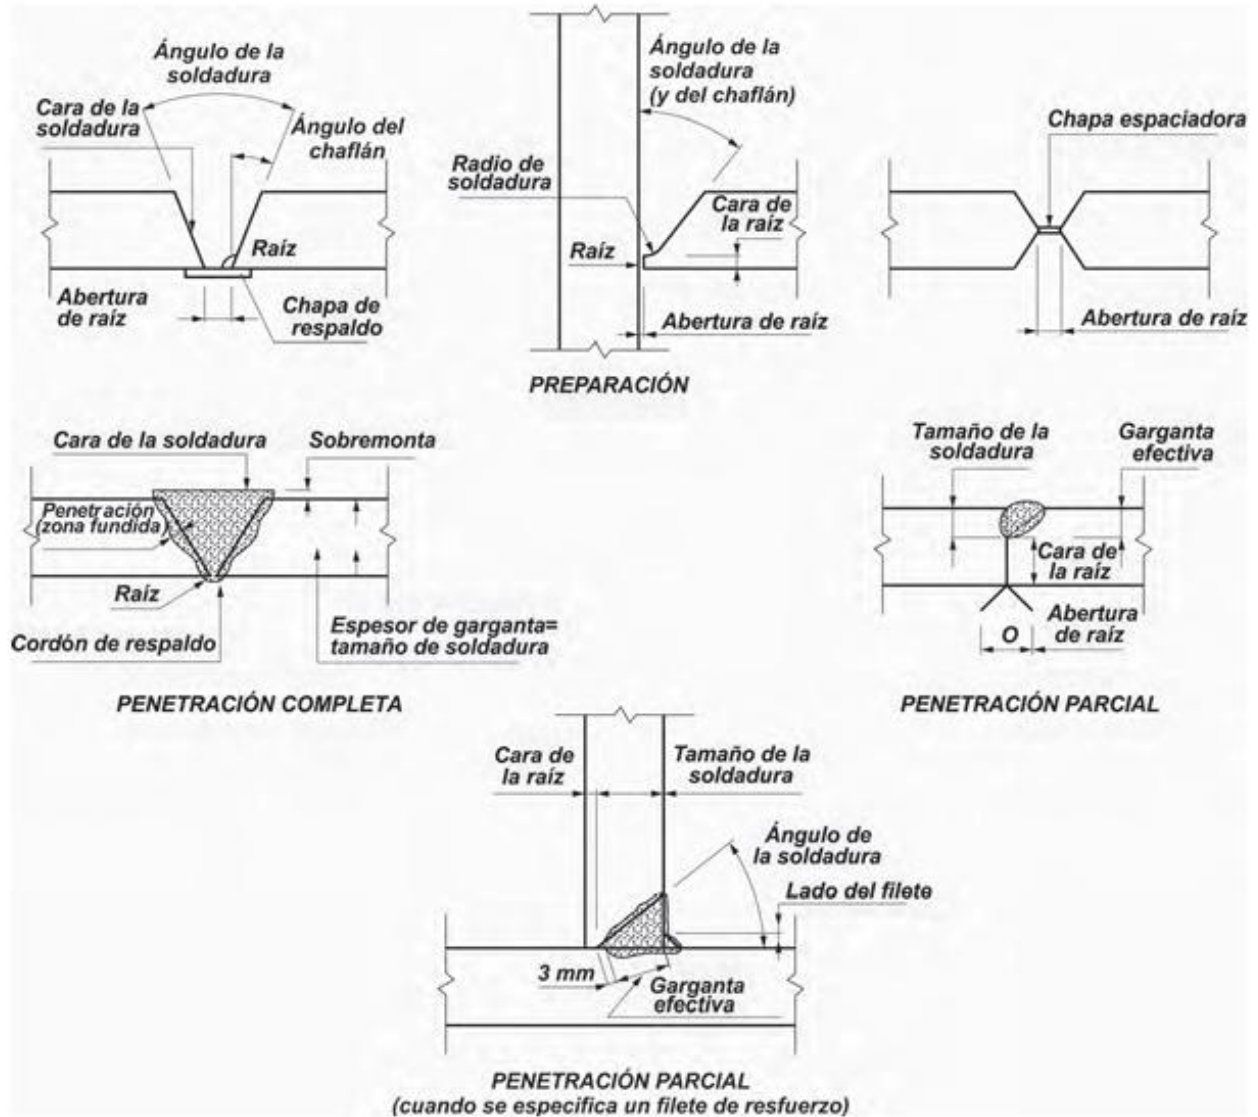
Nomenclatura de soldadura a tope.
